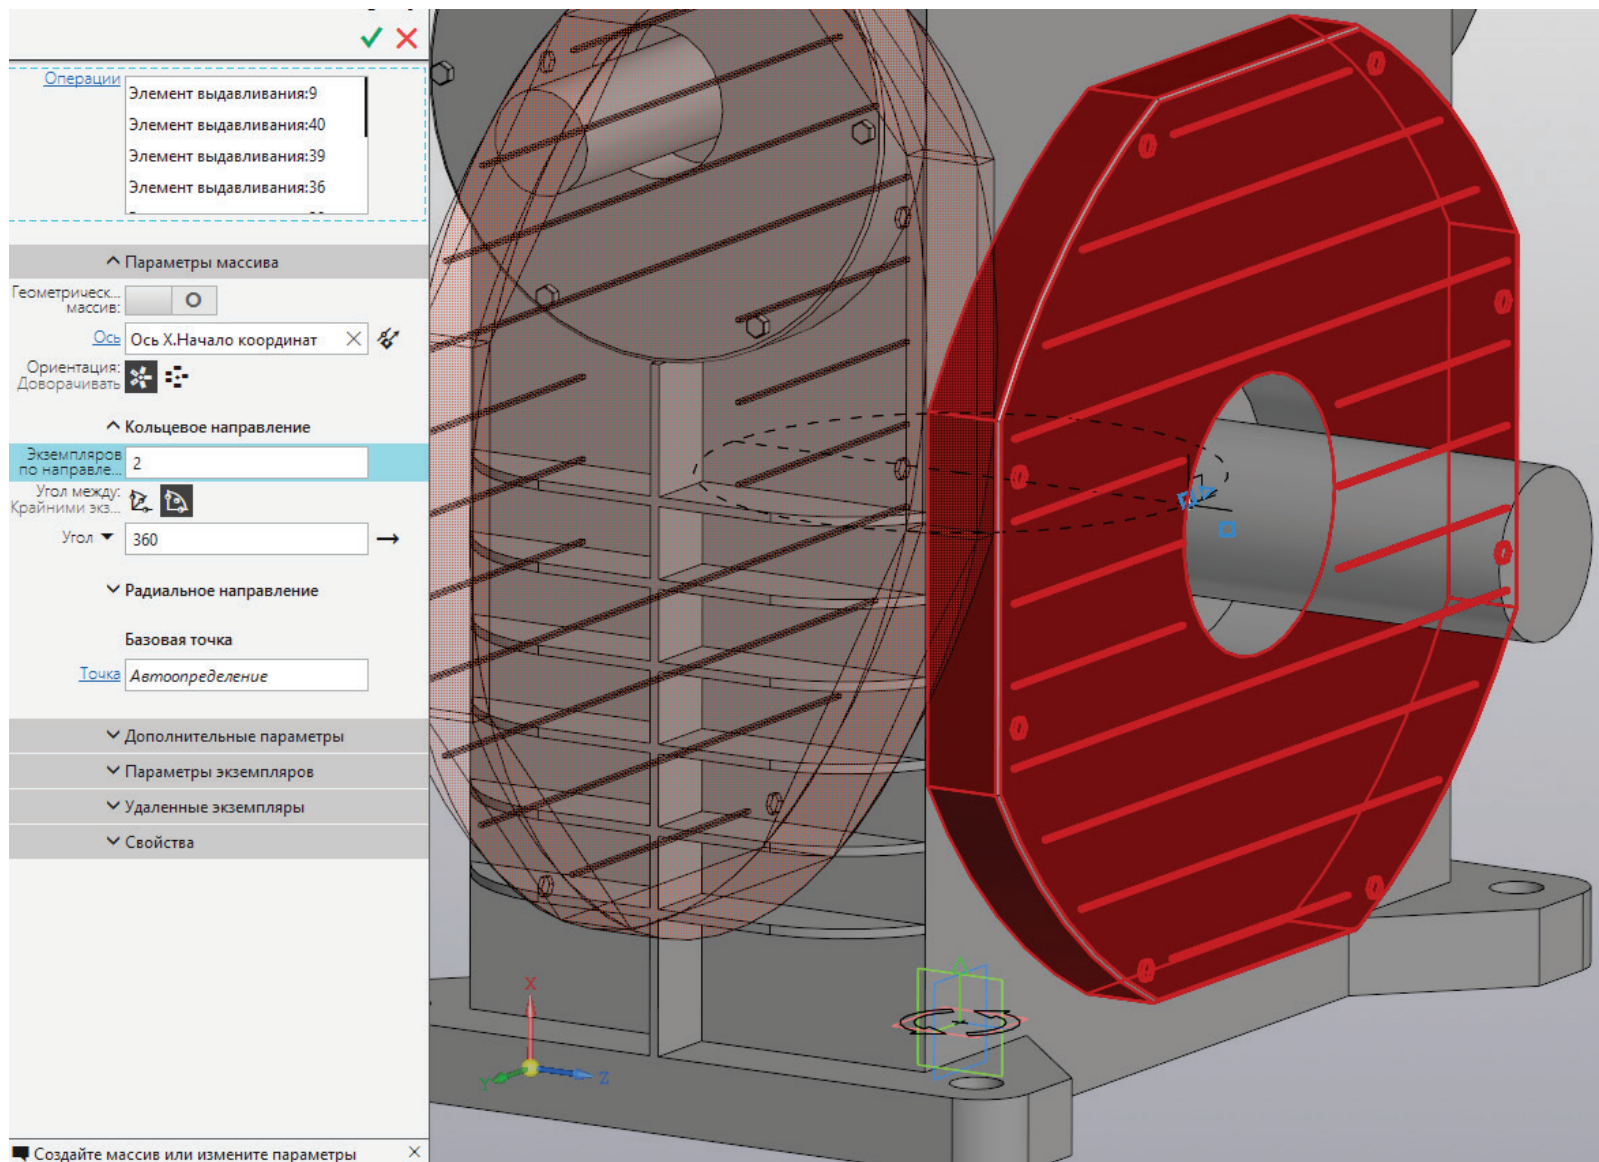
Применение зеркального массива для создания другой крышки выходного вала редуктора
